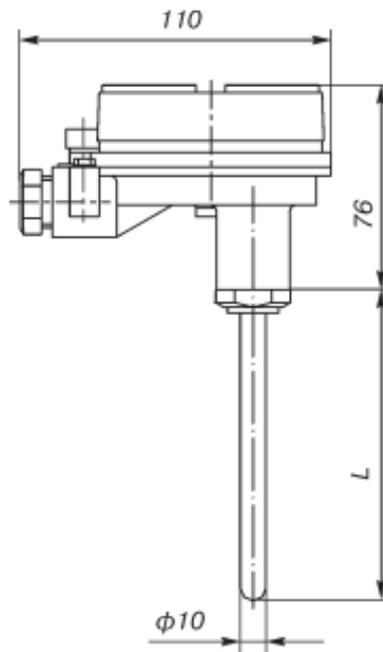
Габаритные и присоединительные размеры Метран-286
